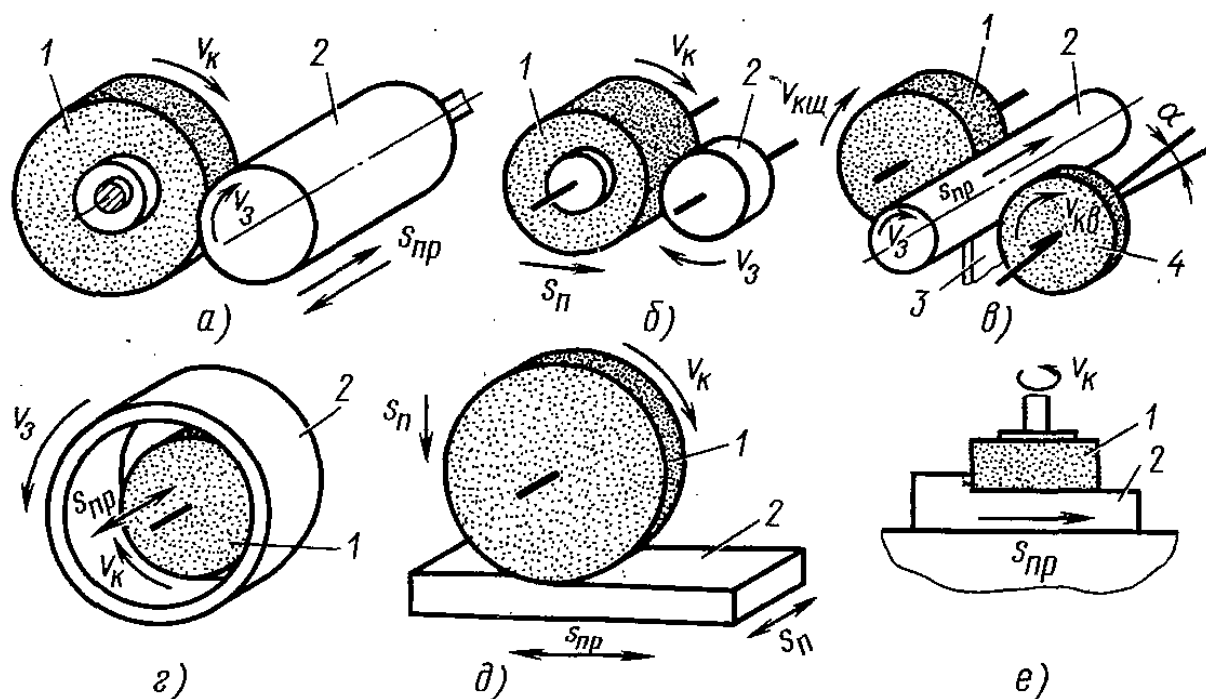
Схеми основних видів шліфування: а, б – круглого зовнішнього; в – круглого безцентрового; г – круглого внутрішнього; д – плоского периферією круга; е – плоского торцем круга; 1 – шліфувальний круг; 2 – заготовка; 3 – опорний ніж; 4 – ведучий круг
